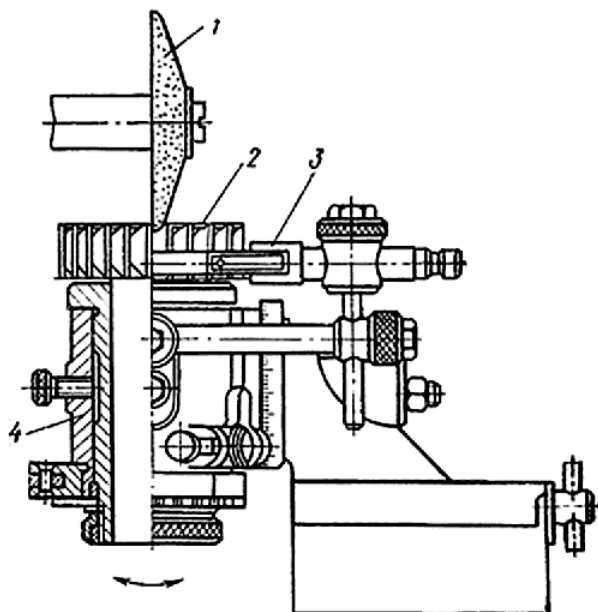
Заточка передней поверхности торцового зуба трехсторонней пазовой фрезы в малой универсальной головке:
